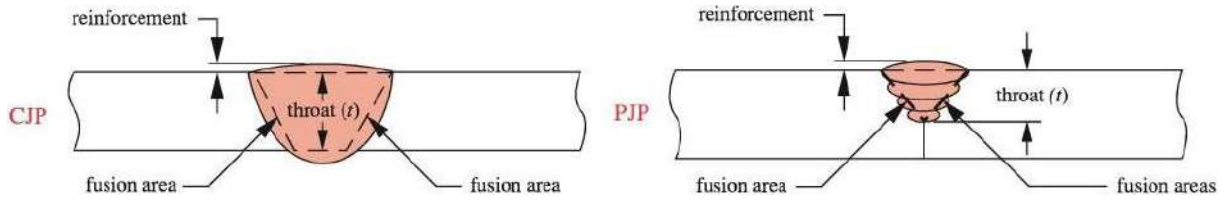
Esquema de juntas soldadas CJP y PJP.
